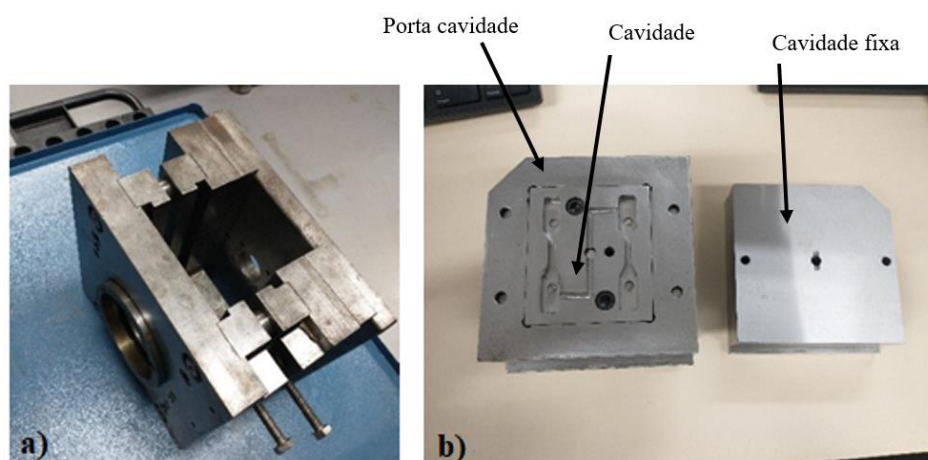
Ferramental para moldagem por injeção, a) porta molde e b) cavidades com o inserto de aço ajustado
